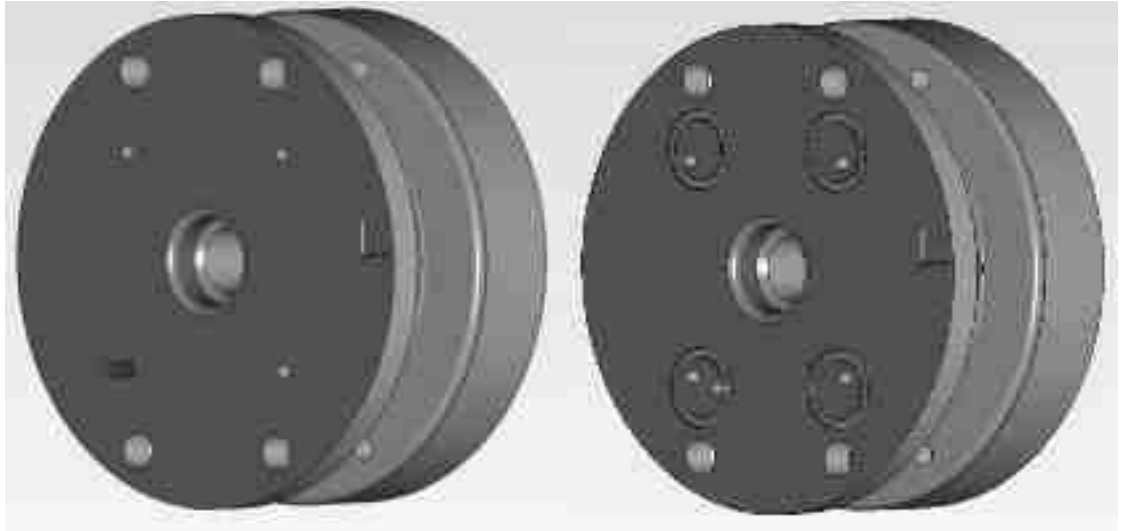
Сверление отверстий и фрезерование колодцев
